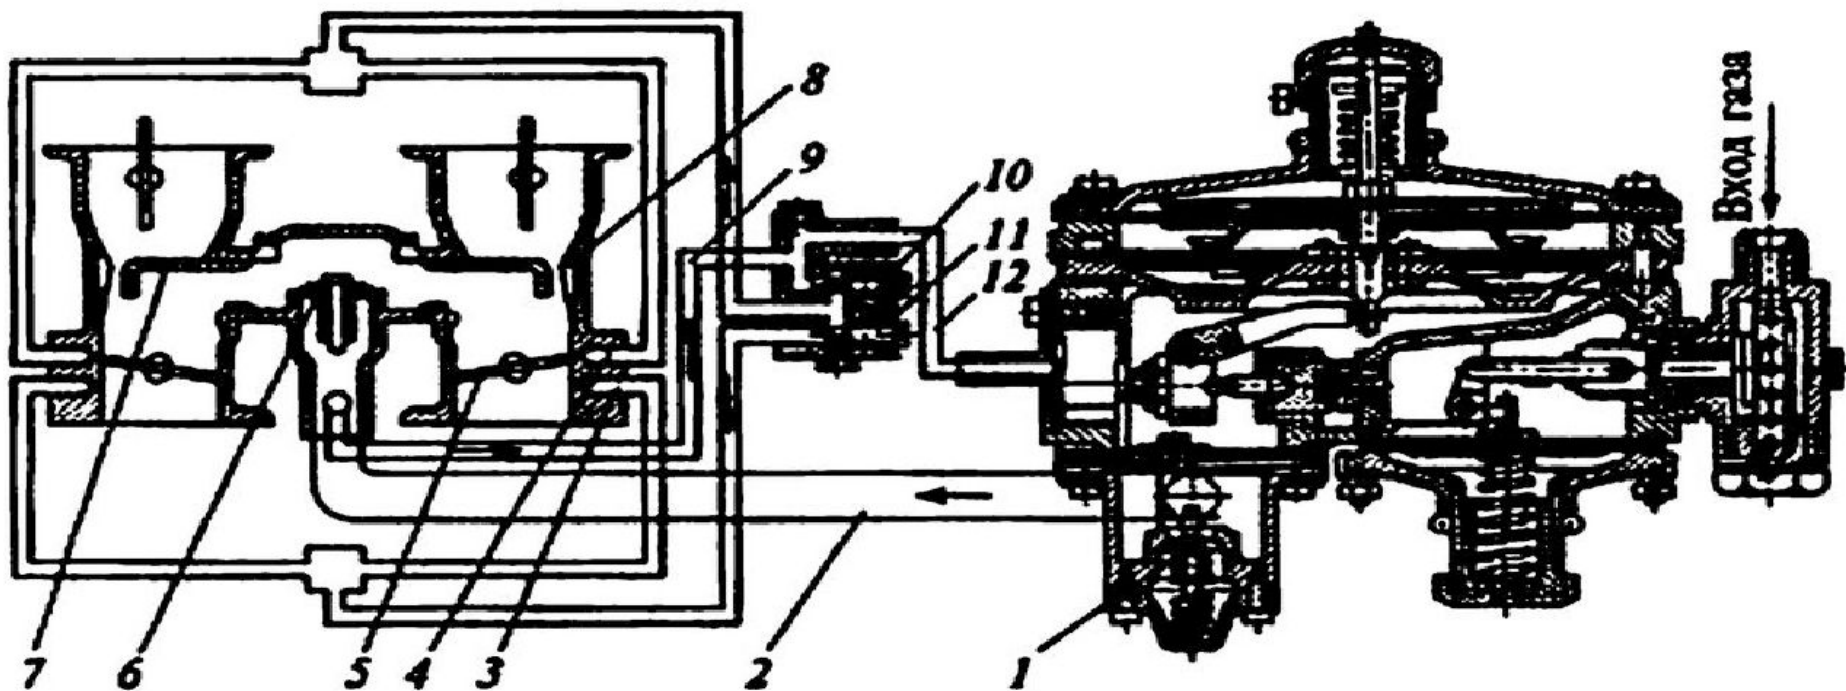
Схема соединения газового смесителя и двухступенчатого редуктора:
